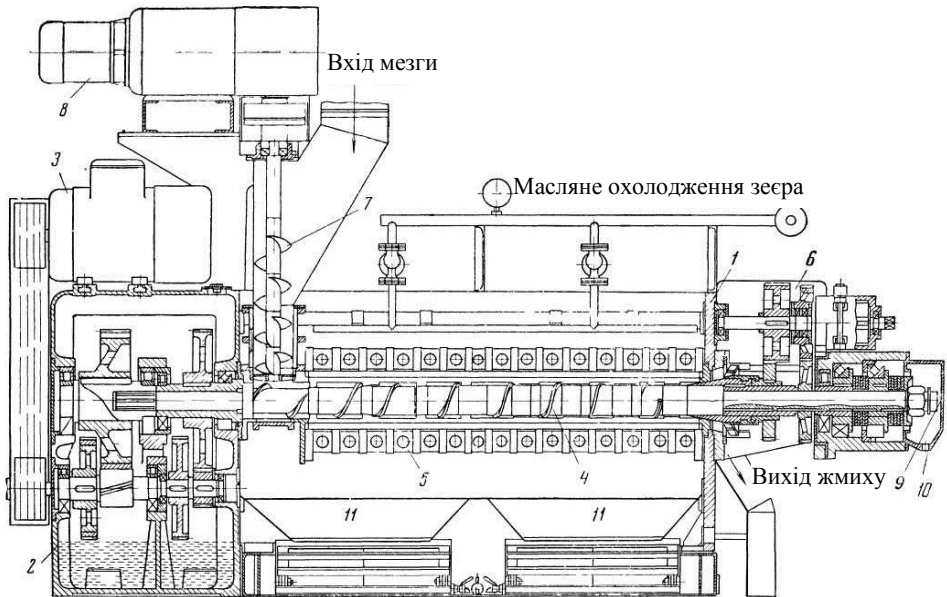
Прес ЕТП-20: 1 – корпус преса; 2 – редуктор; 3 – електродвигун; 4 – шнековий вал; 5 – зєрний циліндр; 6 – механізм переміщення конуса; 7 – шнековий живильник; 8 – електродвигун живильника; 9 – патрубок для подачі води, що охолоджує; 10 – патрубок для води, що відходить; 11 – масляний піддон
